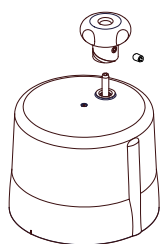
EA-C 20 - 80 Befestigungsschraube lösen
